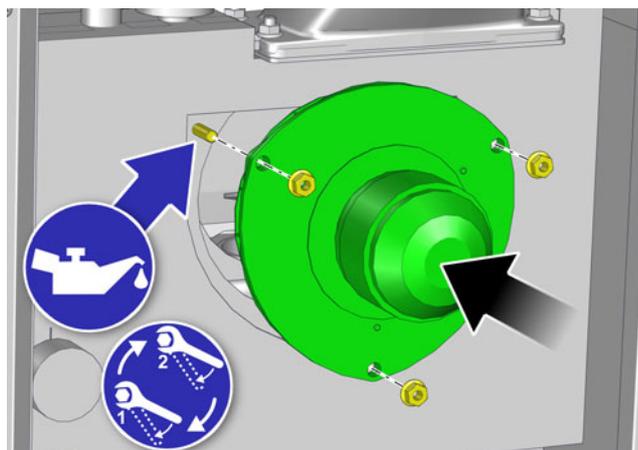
Nettoyage du rotor et remplacement du joint
